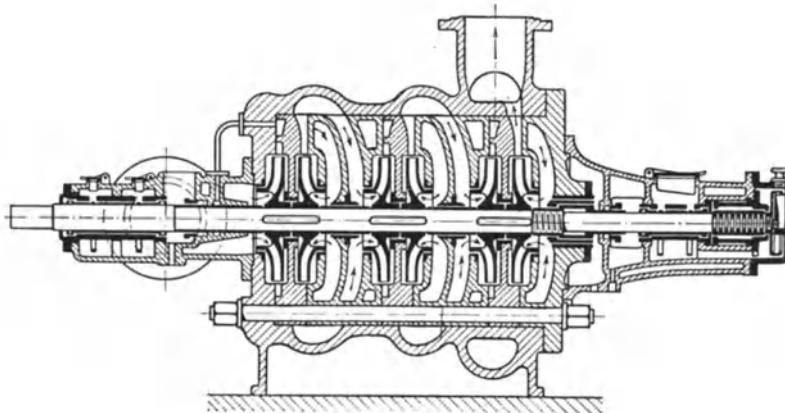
Hochdruck-Zentrifugalpumpe. II. Ausführung.
